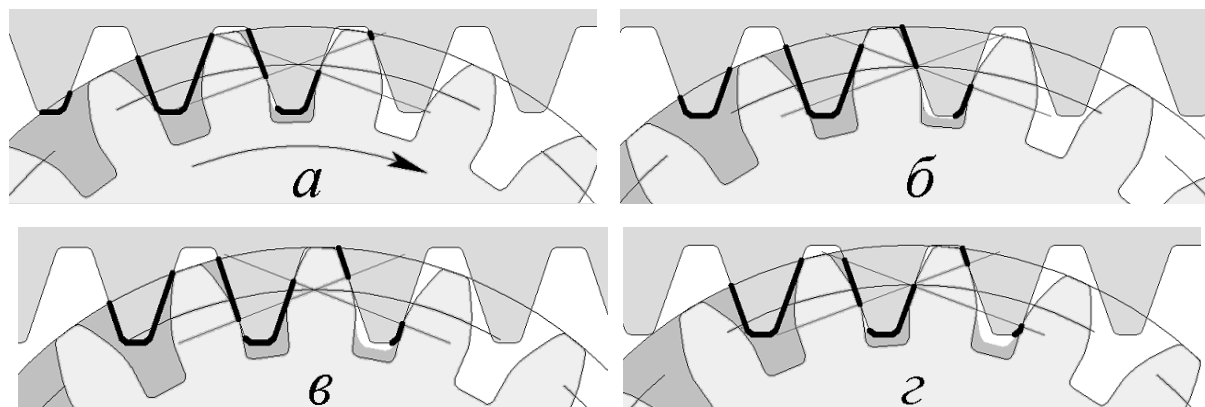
Контакт фрезы (сверху) с заготовкой (снизу) в проекции 2 в четырех угловых положениях: а, б, в, г
